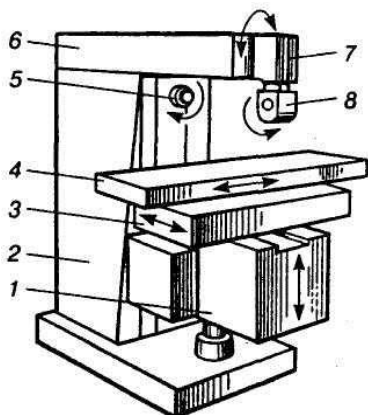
Горизонтально-фрезерний верстат: 1 – консоль;
